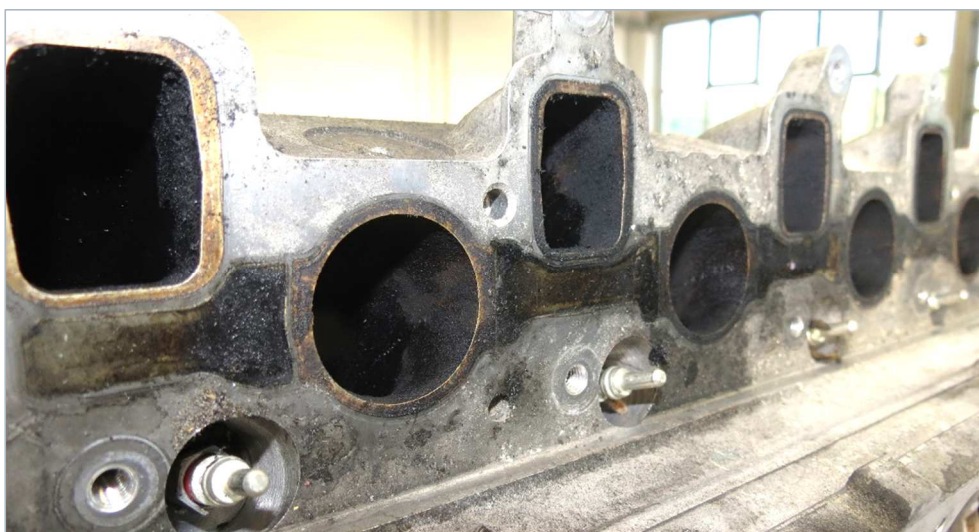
Einlasskanäle des Zylinderkopfes mit Rußablagerungen (Ausgangszustand)
